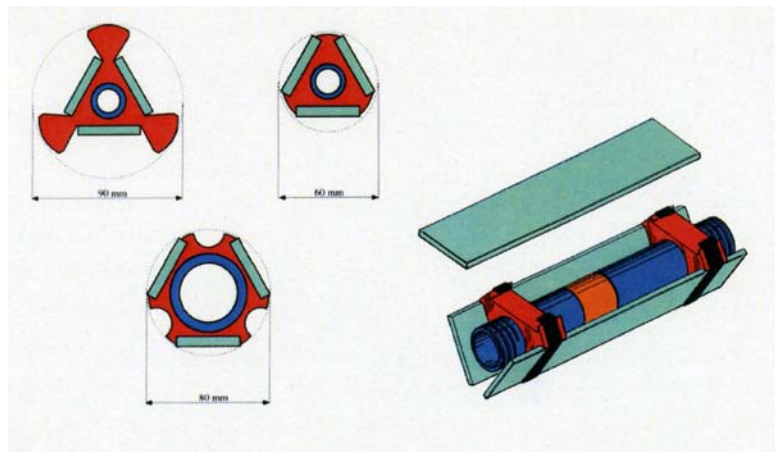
Detalle cabeza de bulón de tiras de fibra de vidrio.
